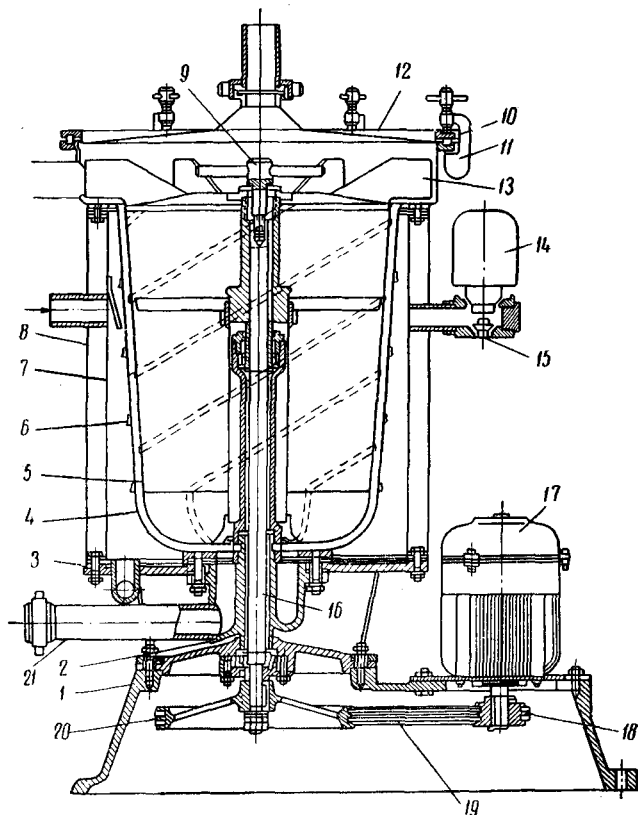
Паровой пастеризатор ОПМ с вытеснительным барабаном:
